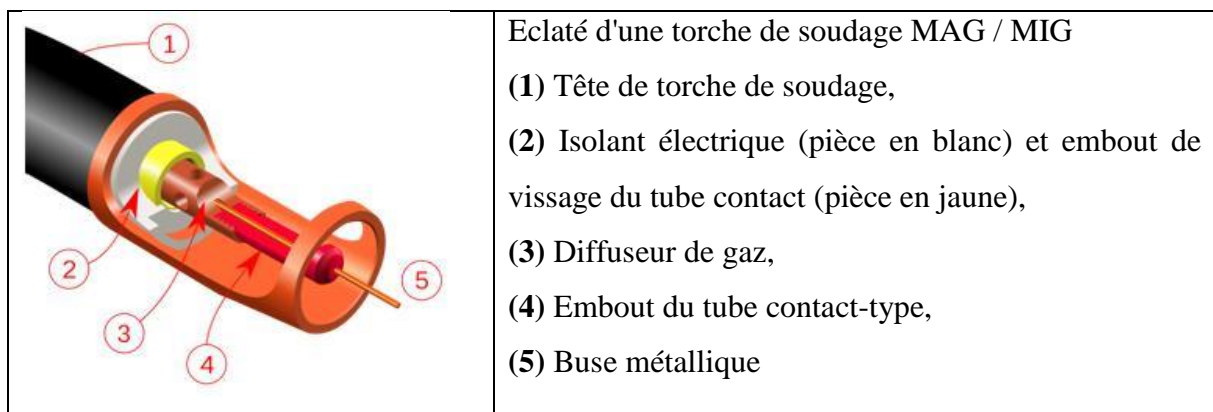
Schémas de la torche de soudage semi-automatique
